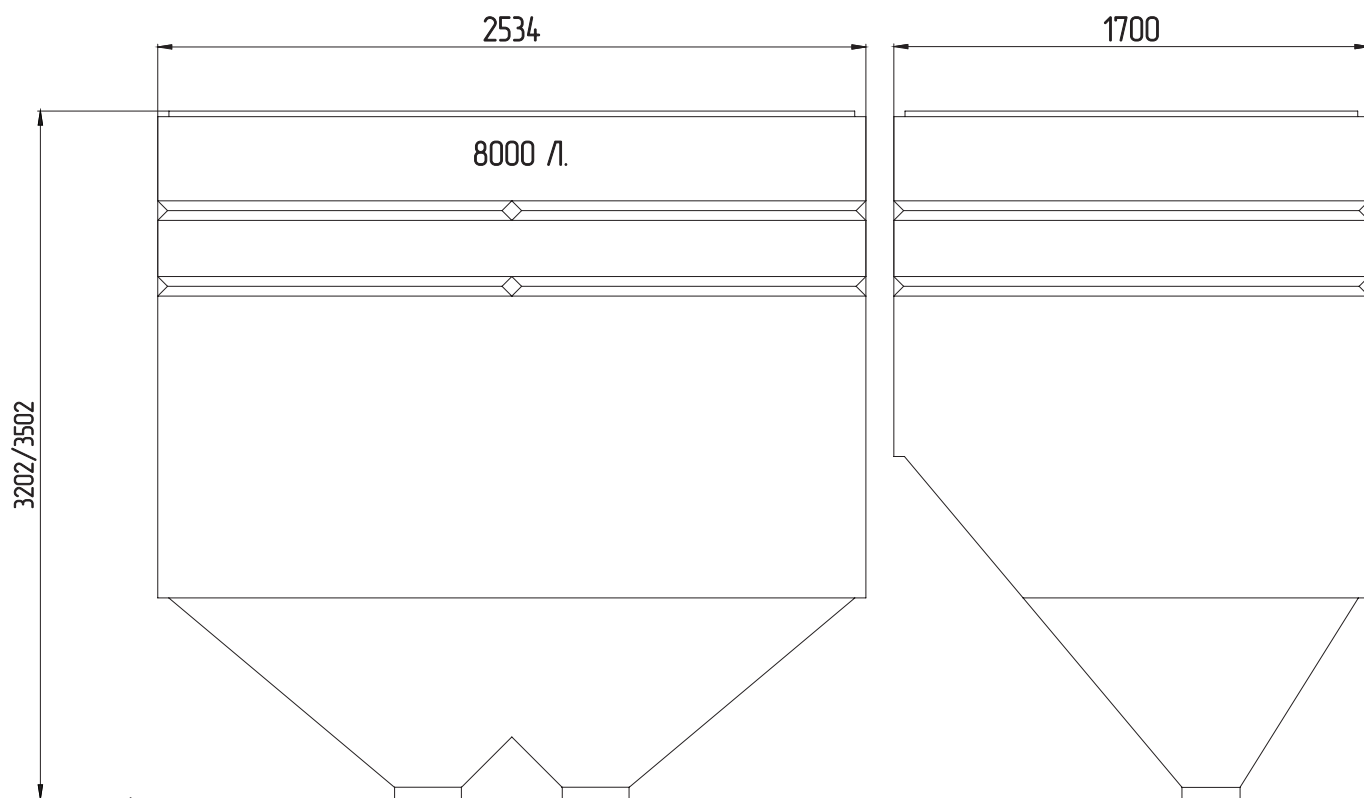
Габаритные размеры топливного бункера 8000 л 2 горла
